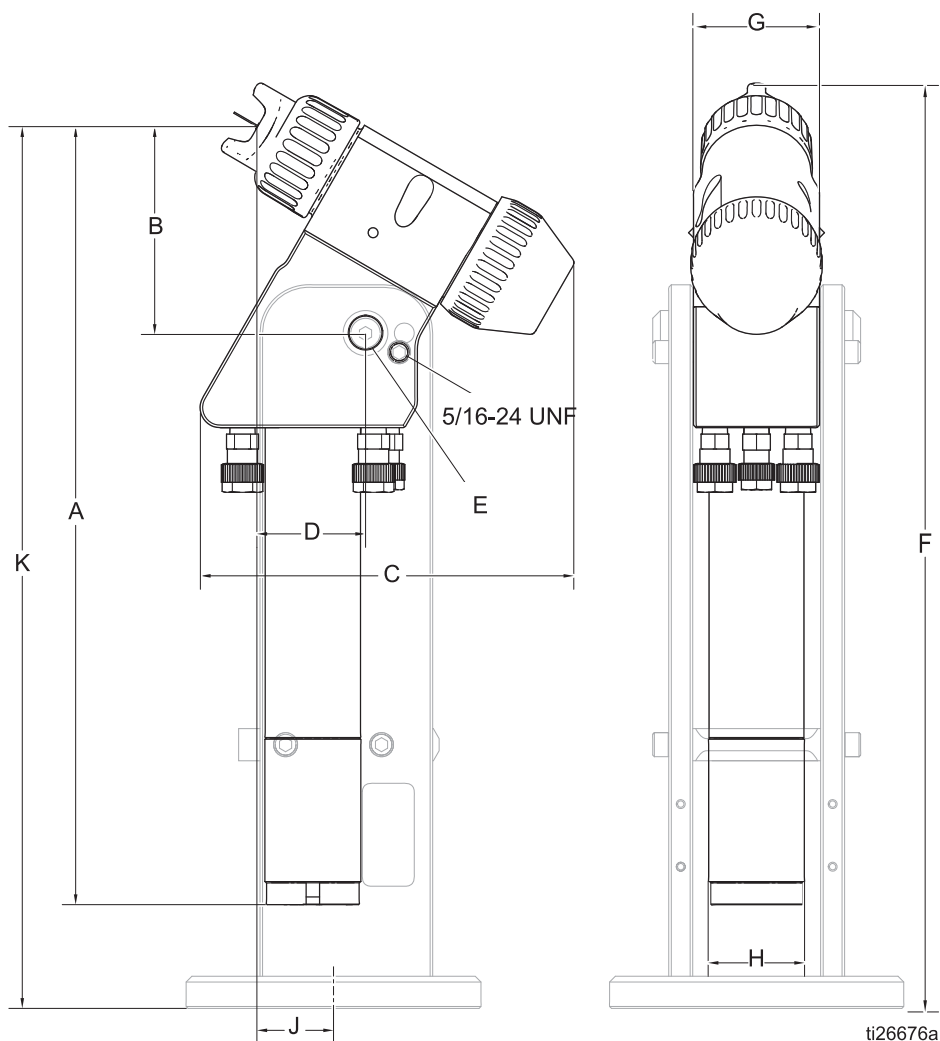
Pistola per montaggio posteriore - Dimensioni
